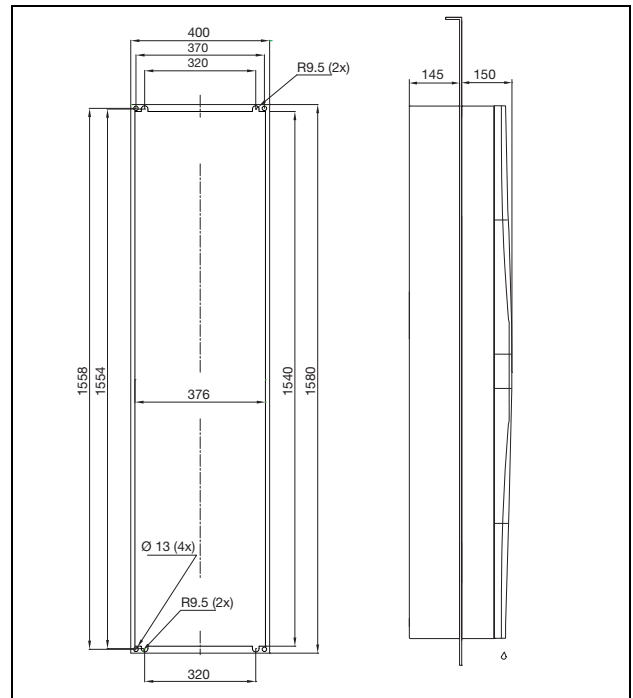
3304.xxx, 3305.xxx – montaż częściowo wewnętrzny
